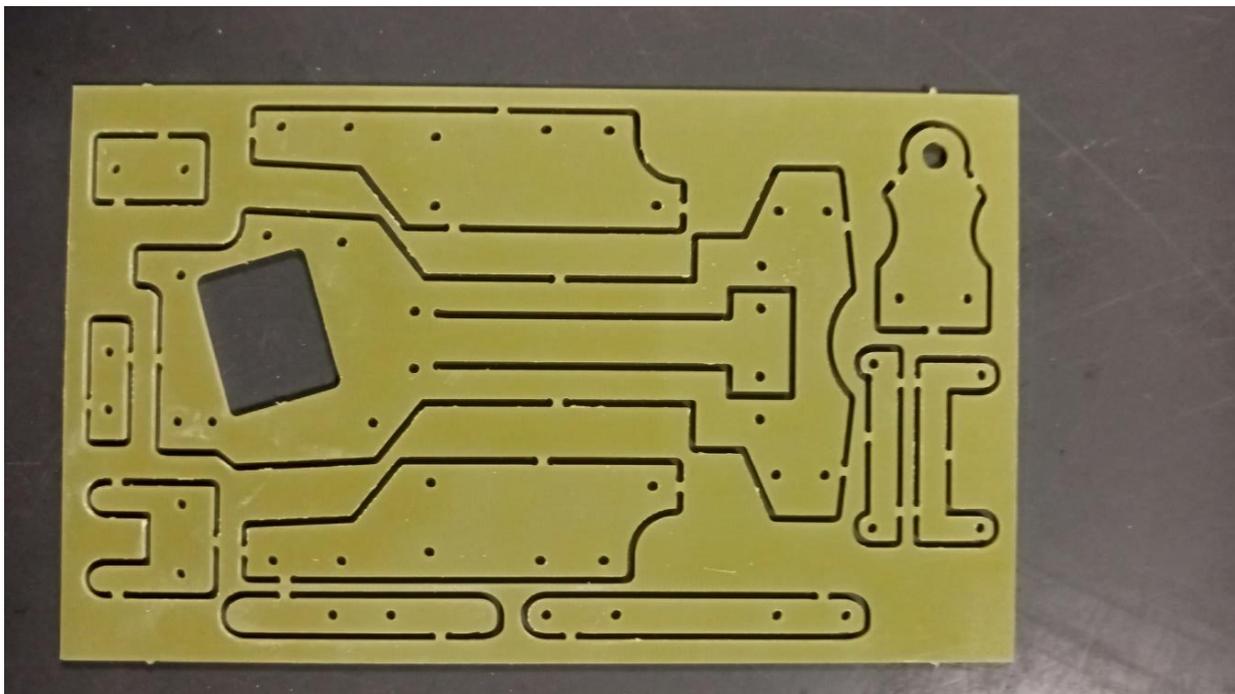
Пример заготовки шасси, выполненной на фрезерном станке с ЧПУ.
